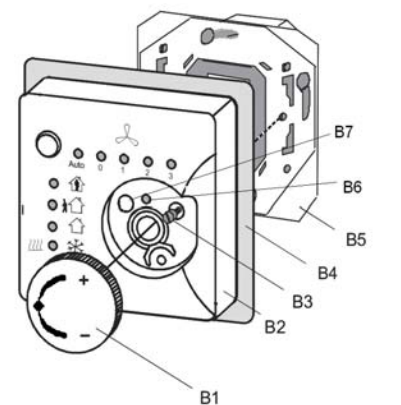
Montage des Fan-Coil Unit Bediengerätes
